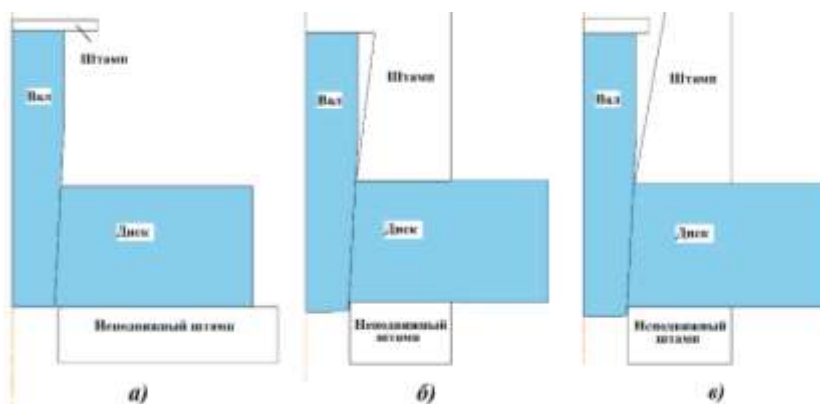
Конечно-элементная модель детали «диск-вал» для сварки по Схеме 1 (а), Схеме 2 (б) и Схеме 3 (в).
